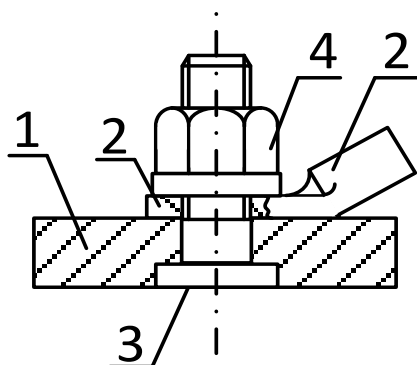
Контактное соединение шин ШУП-МВДР и ШУП-МДВДР через винт запрессовочный (1 - медная шина; 2 – кабельный наконечник; 3 – винт запрессовочный; 4 – гайка с зубчатым фланцем).
